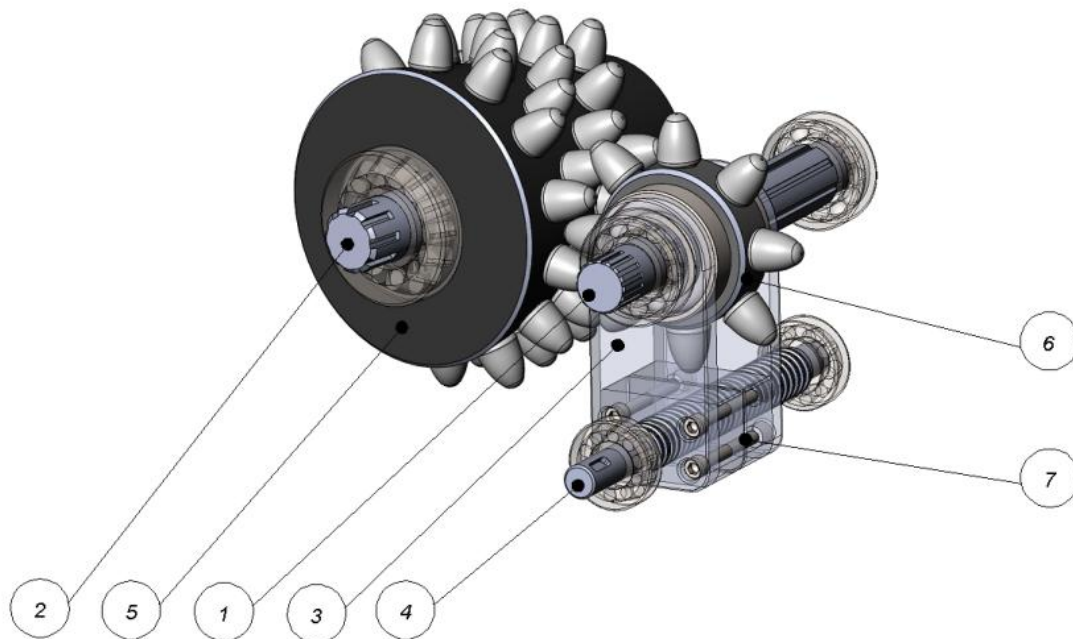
Зубчастий варіатор: 1 – вал ведучий; 2 – вал ведений; 3 – кронштейн механізму регулювання передавального числа; 4 – гвинт механізму регулювання передавального числа; 5 – конусне зубчасте колесо; 6 – шестерня з ковзаючою муфтою; 7 – стяжний гвинт
